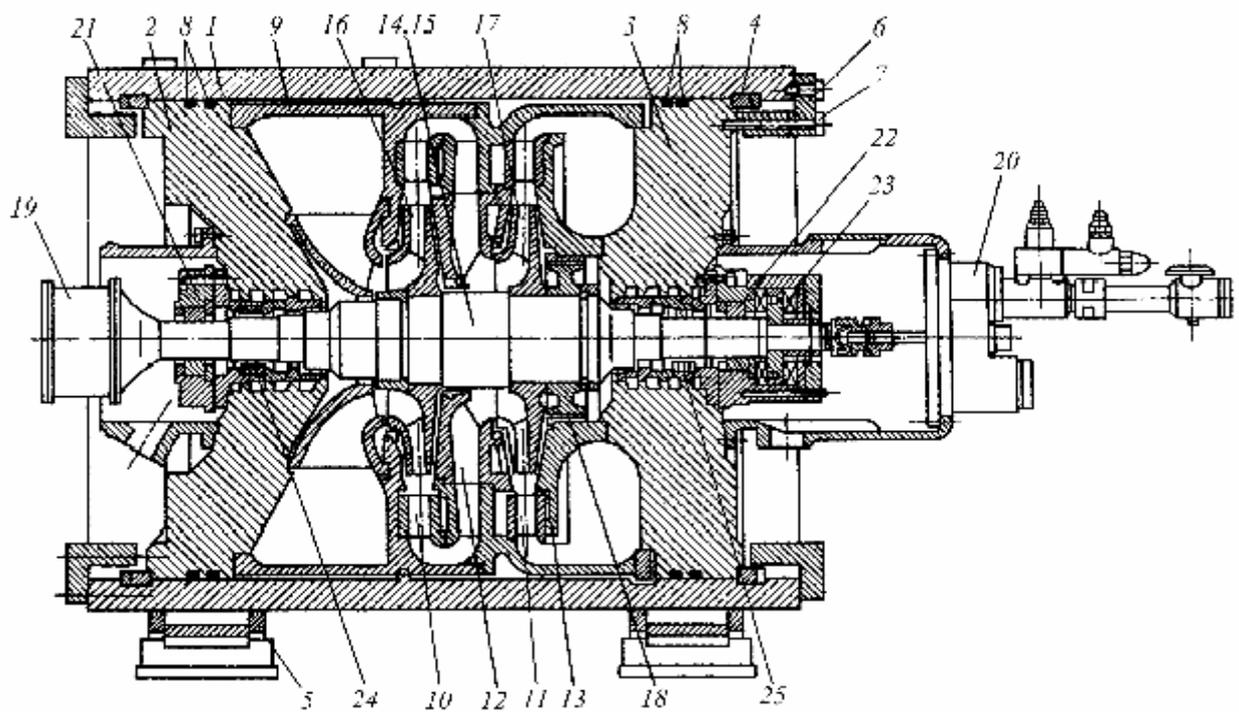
Двухступенчатый центробежный компрессор с вертикальным разъемом корпуса ГПА-Ц-16 [2]
